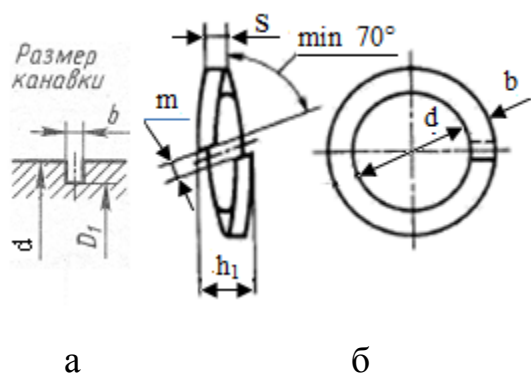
Изображение канавки для стопорящих деталей (а), пружинной шайбы (б)
